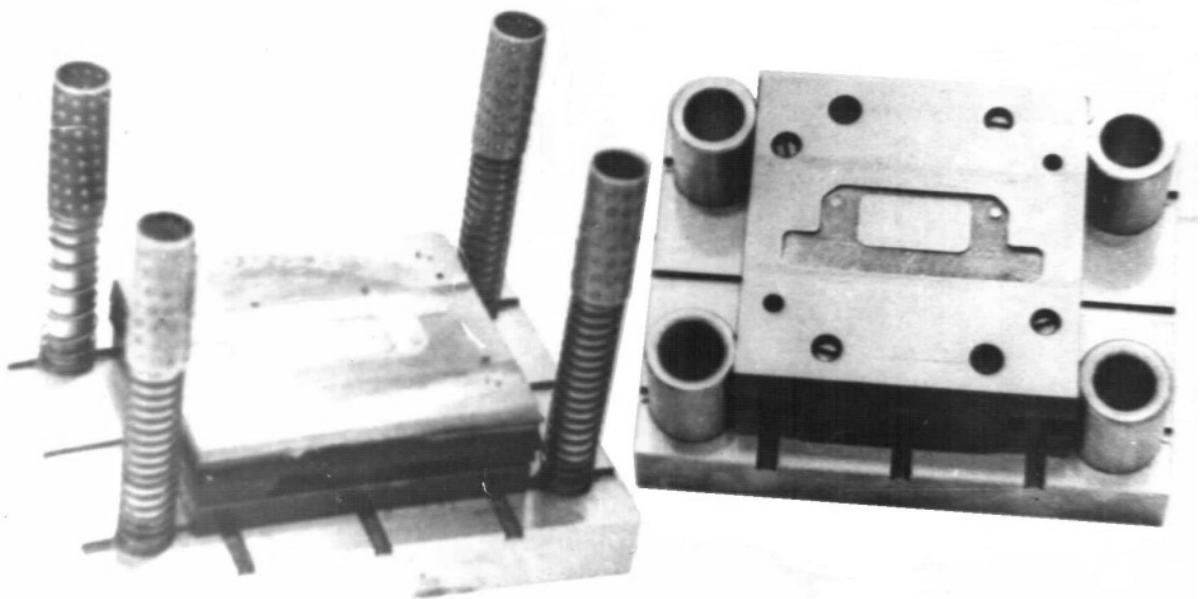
Универсально-сборный штамп с шариковыми направляющими.
